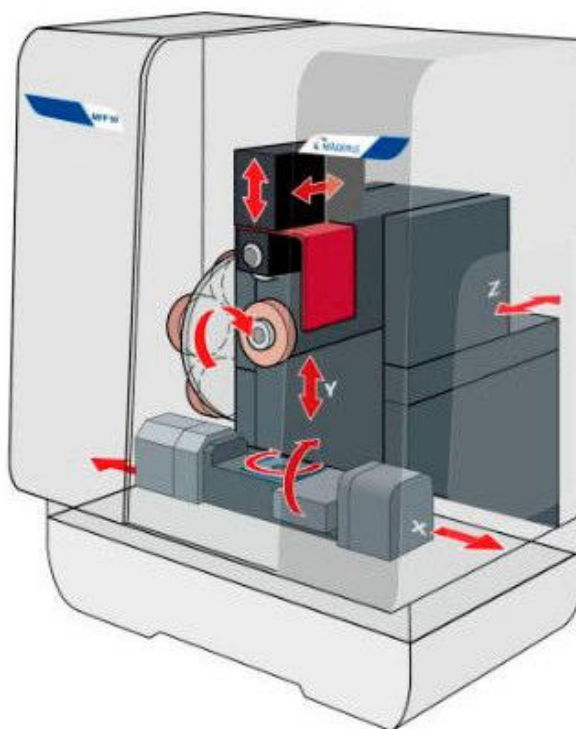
Компоновка станка модели MFP-50.65.65 и его кинематическая схема
